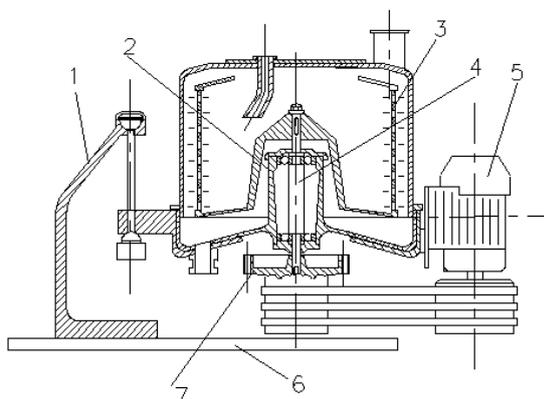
Маятниковая центрифуга типа ФМБ (Б - через борт) с верхней выгрузкой осадка: 1 - колонны; 2 - корпус привода; 3 - ротор; 4 - вал; 5 - электродвигатель; 6 - фундаментная плита; 7 - тормоз
